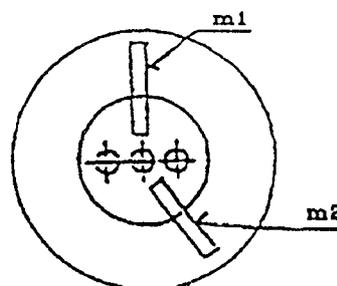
RESERVOIRS A SOUDURES LONGITUDINALES ET CIRCULAIRES, EMPLACEMENT DES EPROUVETTES
